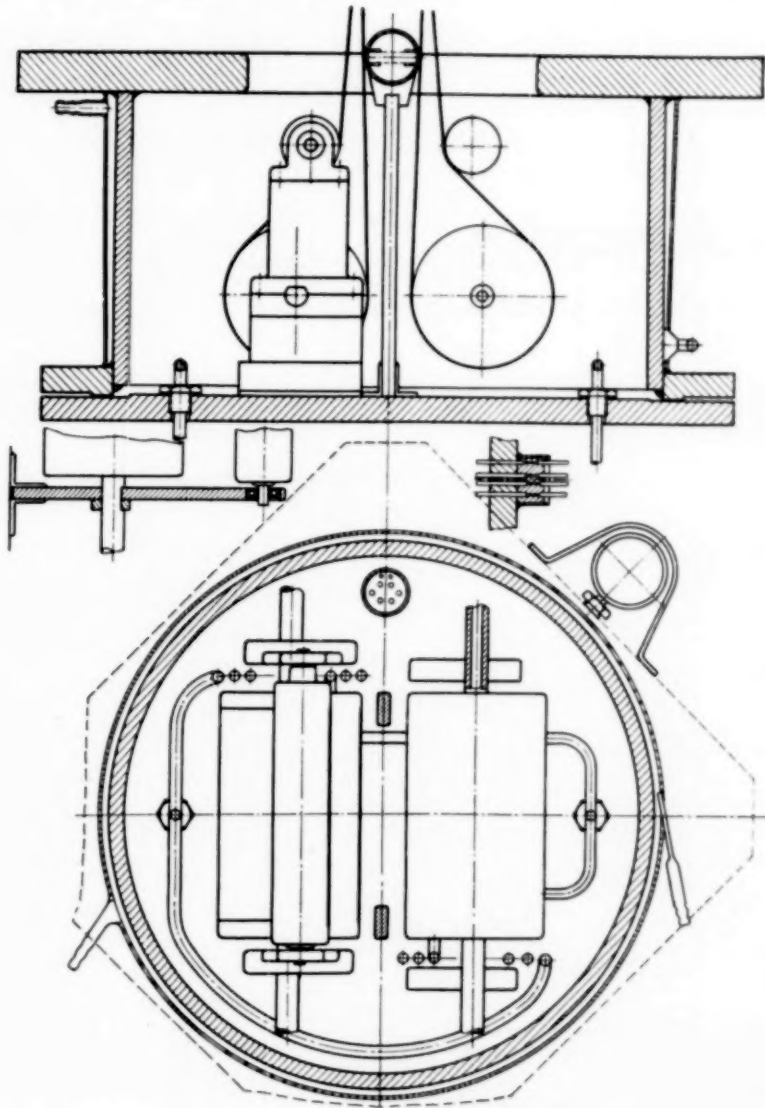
Werkstattzeichnung des unteren Eisenkastens.
